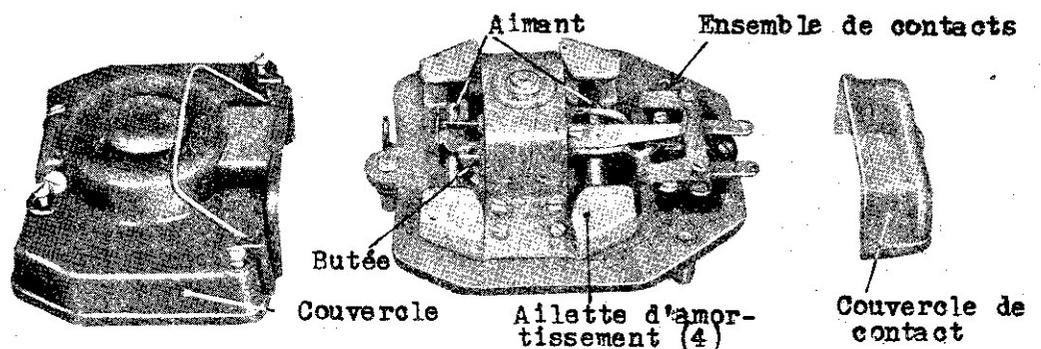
C - Maître compas Mk.IA, ensemble magnétique avec couvercles enlevés.
